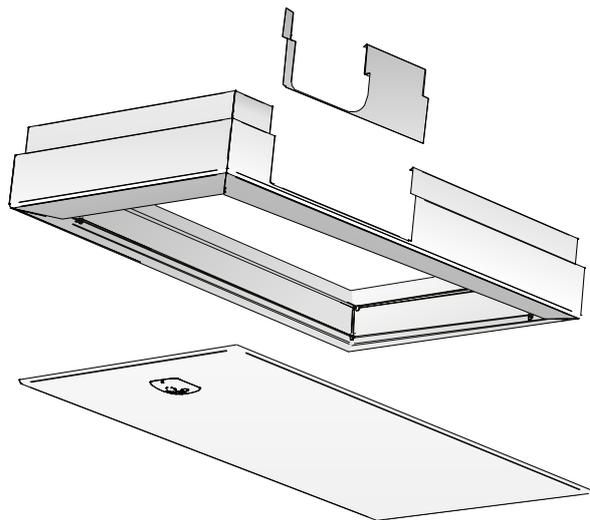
Designmodul mit Abdeckblech sowie Unterblech mit Sensormodul
